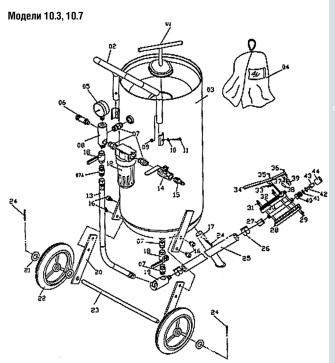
Сборочный чертёж 10.3, 10.7
